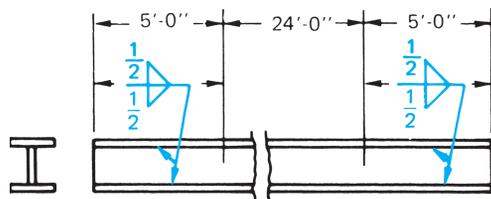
■ Longueur des soudures d'angle spécifiées suivant la procédure de dimensionnement courante.
